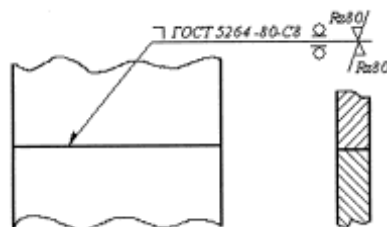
Шов выполнен при монтаже (\square) ручной дуговой сваркой по ГОСТ 5264-80, тип шва)С9), усилие шва снято с двух сторон обработкой резанием (\bigcirc), шероховатость обработанной поверхности с лицевой стороны ∇ $Rz80/$, с обратной стороны ∇ $Rz80$ мкм.
